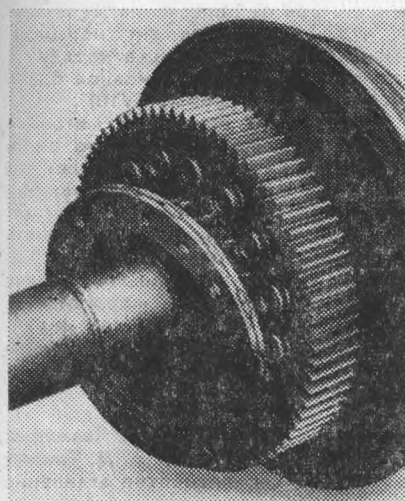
Упругое самоустанавливающееся зубчатое колесо с креплением резино-металлических блоков от осевого смещения ограничительными кольцами, по предложению депо Няндомы
